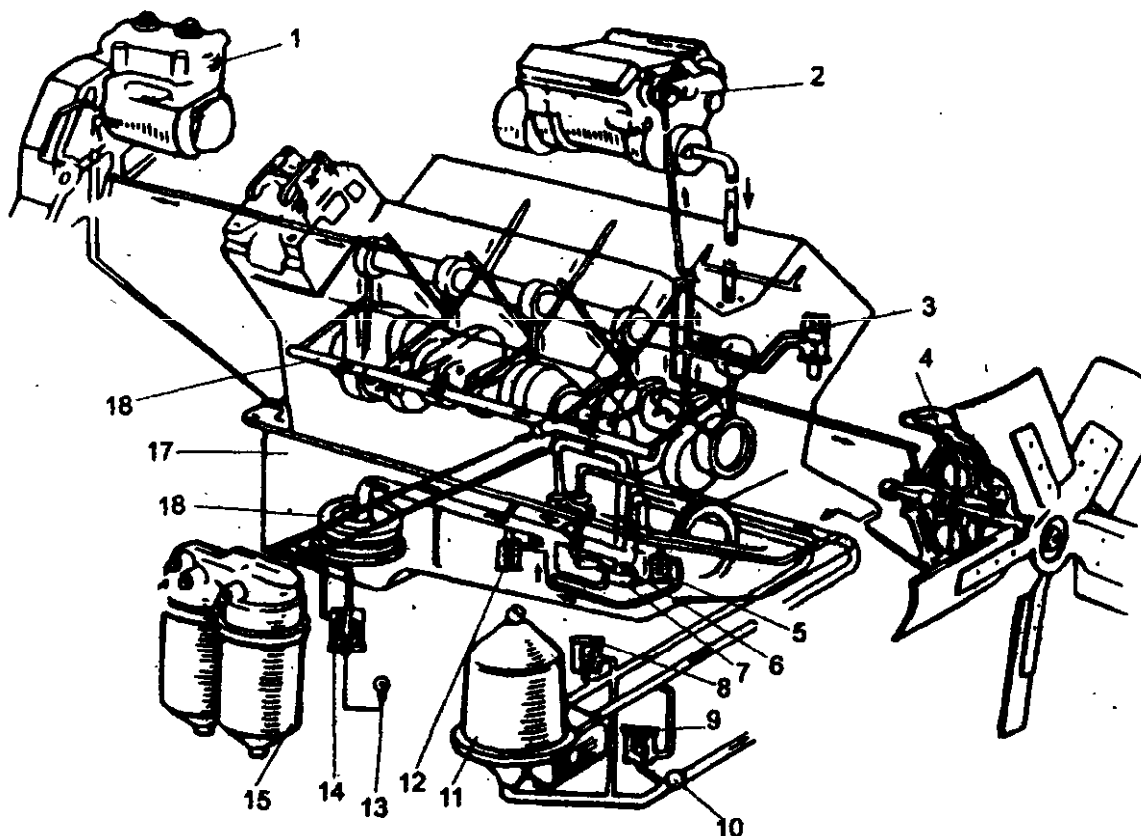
Схема системы смазывания двигателя КамАЗ-740:
